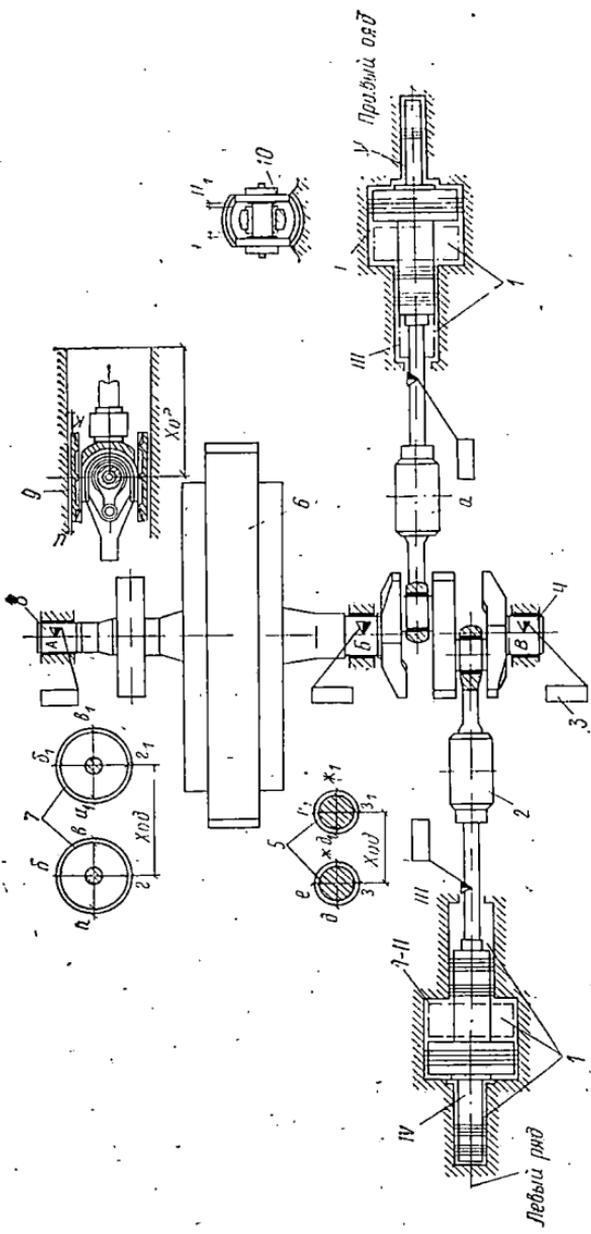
Схема измерения зазоров в механизме движения компрессора
